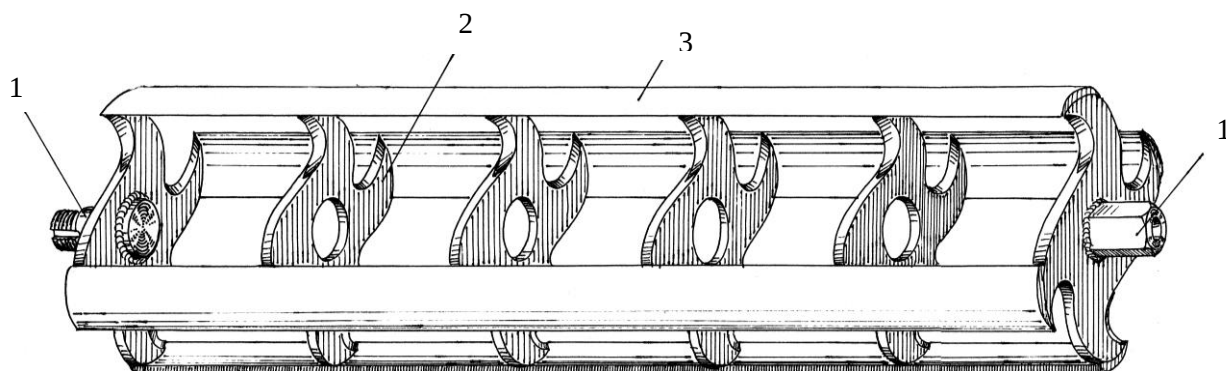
Фрезерный рабочий орган «безвального типа»:
